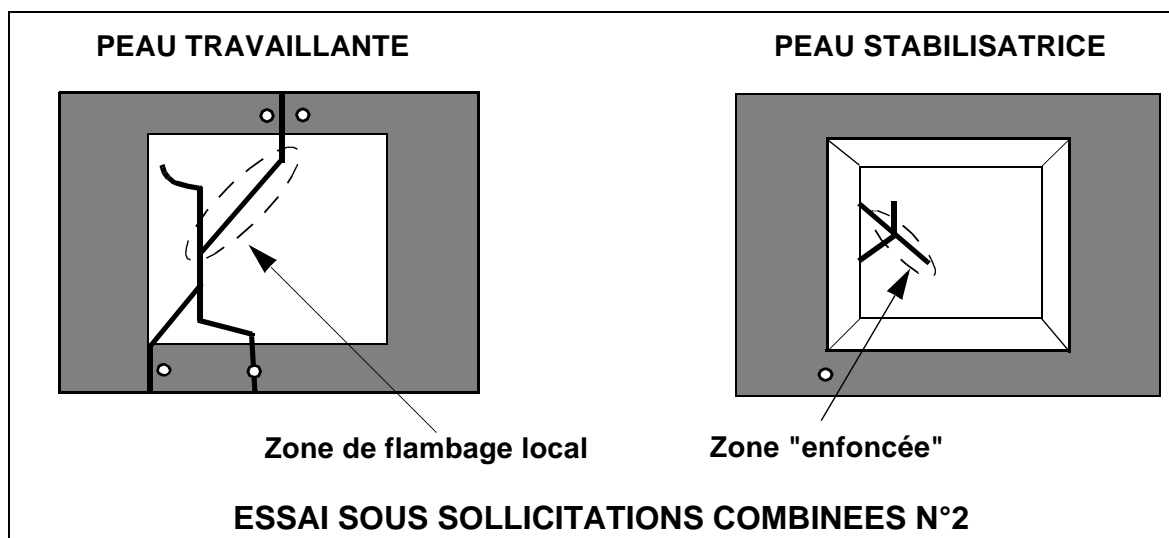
Faciès de rupture essai combinées n°2 (Photo N° A2-13).
